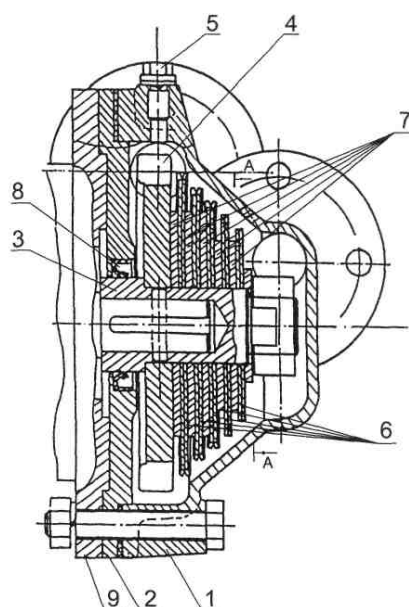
Змішувач-диспергатор DRS 10: 1.Корпус; 2. Диск проміжний; 3. Вал; 4. Крильчатка; 5. Пробка; 6. Диски робітники; 7. Шайби проміжні; 8. Манжета; 9. Електродвигун
